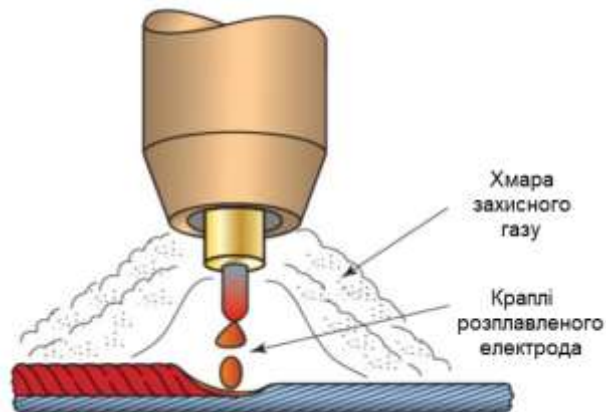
Крупнокрапельний перенос металу в MIG/MAG зварюванні
